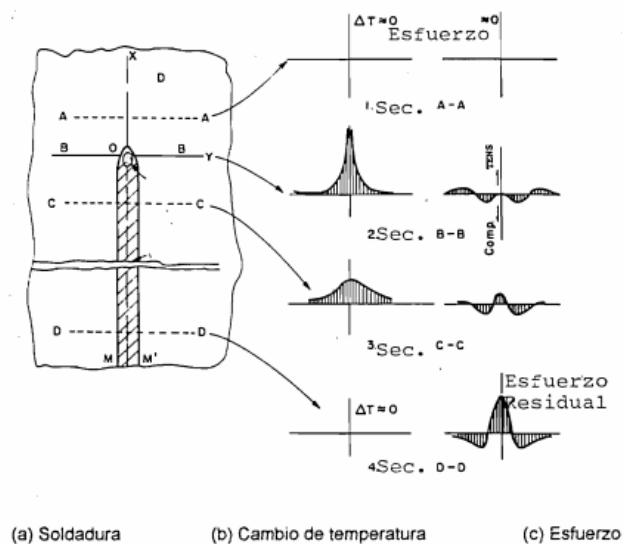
Cambios de temperatura y esfuerzos durante la soldadura.
